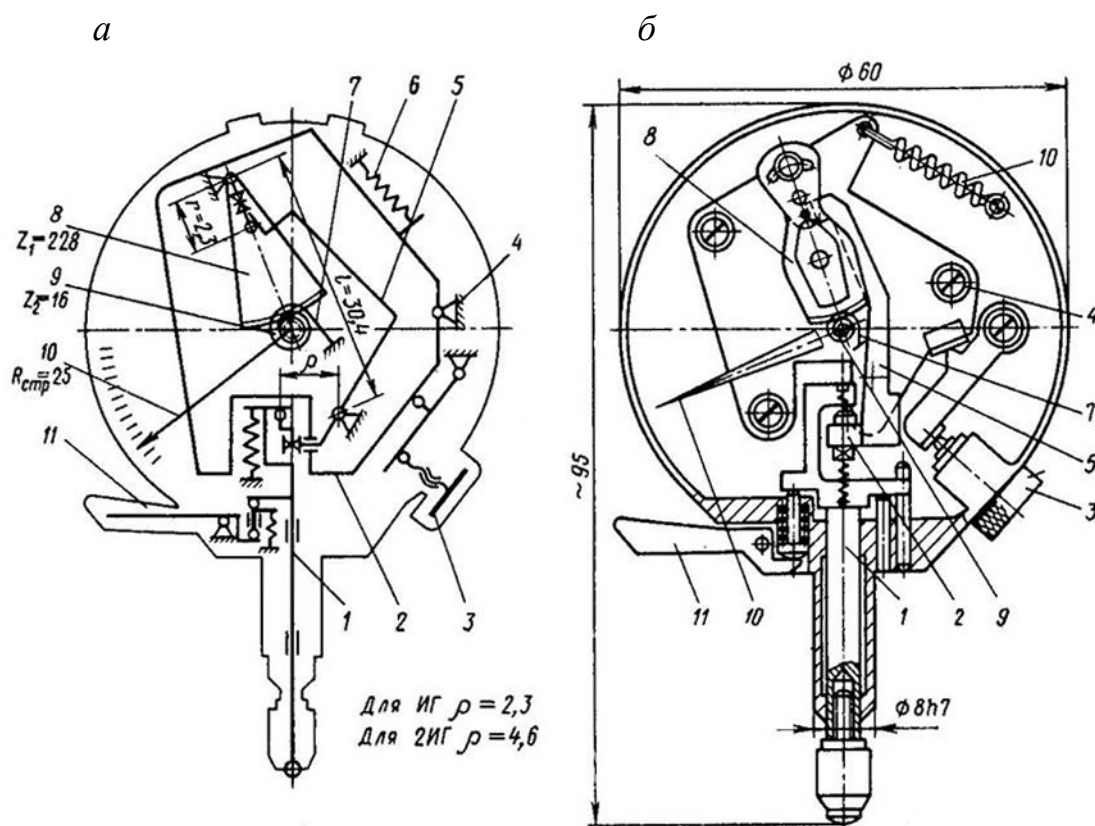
Рычажно-зубчатая головка однооборотная (ИГ):
